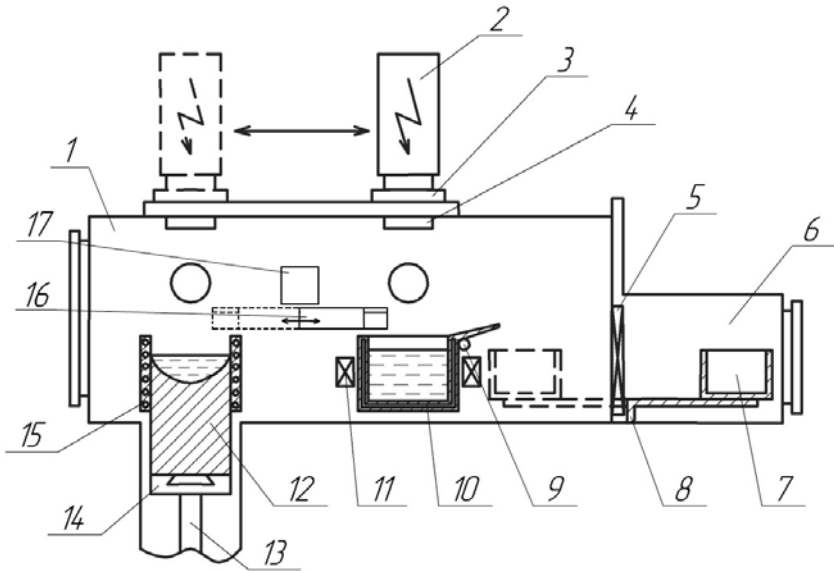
Схема электронно-лучевой установки для получения слитка и литой заготовки: 1 – плавильная камера, 2 – пушка ВТР, обогревающая тигель и кристаллизатор, 3 – подвижная плита, 4, 5 – вакуумные затворы, 6 – камера литейных форм, 7 – блок литейных форм, 8 – устройство перемещения форм, 9 – ось поворота тигля, 10 – тигель, 11 – система ЭМП тигля, 12 – слиток, 13 – механизм вытягивания слитка, 14 – поддон, 15 – кристаллизатор, 16 – промежуточная ёмкость, 17 – устройство подачи шихты
